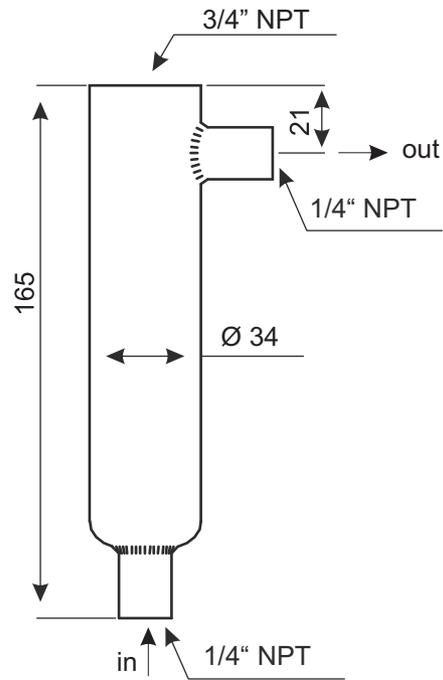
Einschweißstutzen für Sensoren der Serie 8394
